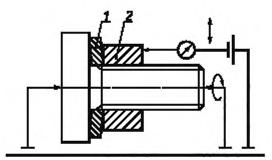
Калибр для проверки лозиционного допуска, установленного на рисунках 76 и 78
